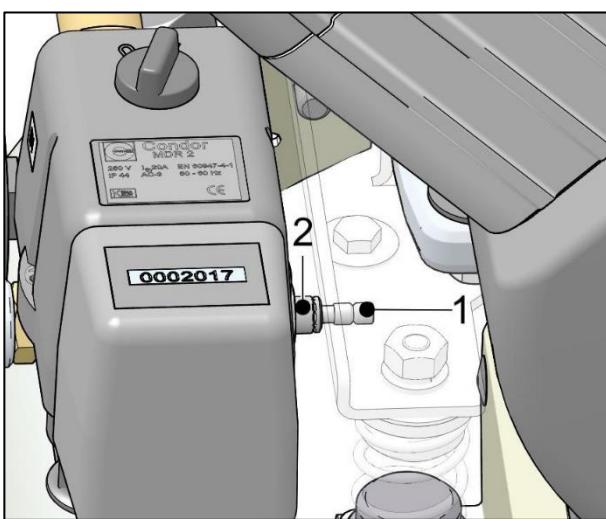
Prijenie k výstupu stlačeného vzduchu
